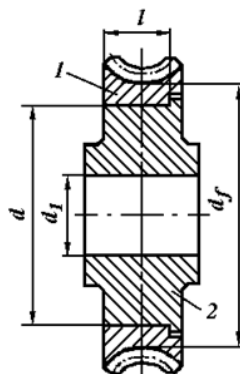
Цилиндрическое соединение с натягом венца червячного колеса с центром
